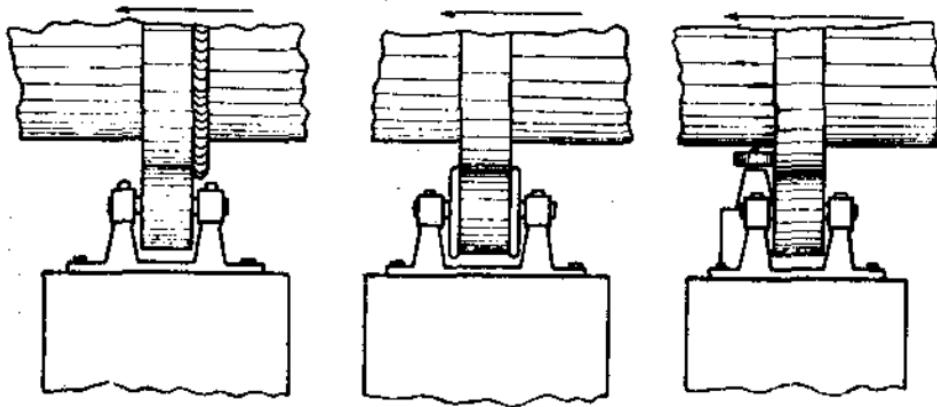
Типы приспособлений для предупреждения осевого сдвига барабана.
